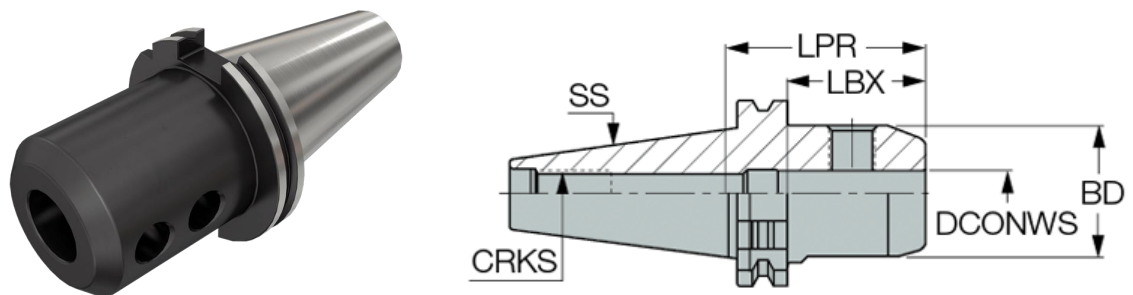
Державка для фрез DIN69871 40 EM32X100
